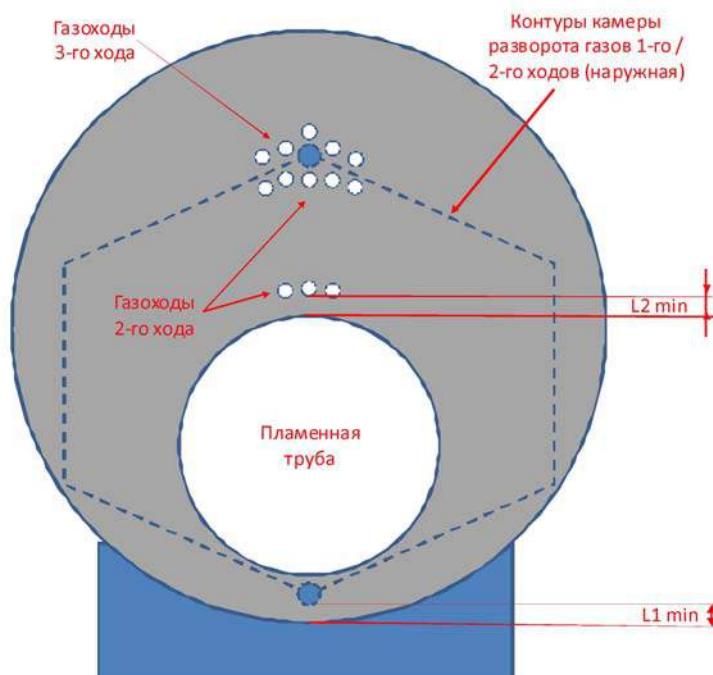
Котёл с наружной камерой разворота газов (вид спереди)
